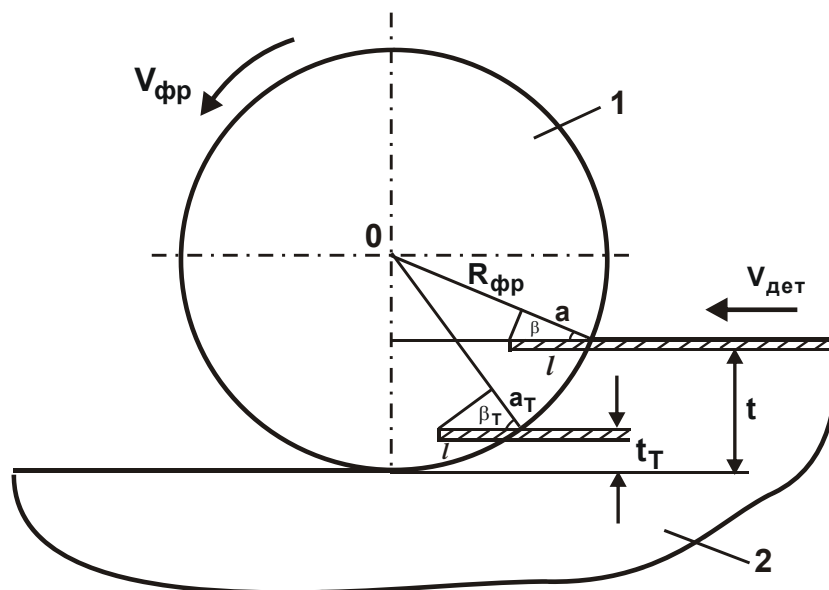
Расчетная схема параметров фрезерования цилиндрической фрезой: 1 – контур фрезы; 2 – обрабатываемая деталь
